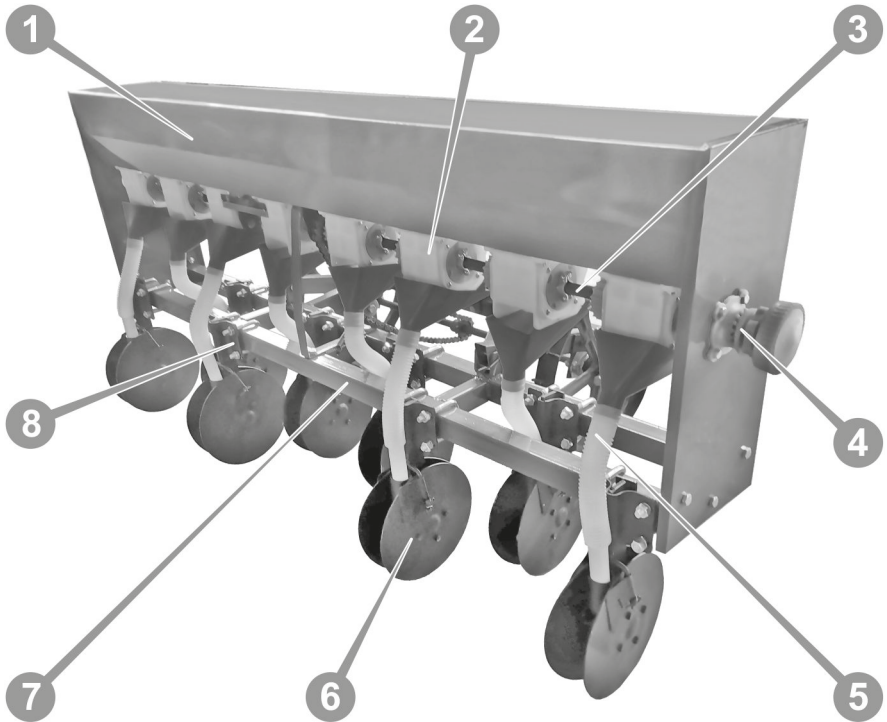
Сівалка СЗ-6 дискова (вигляд ззаду)
